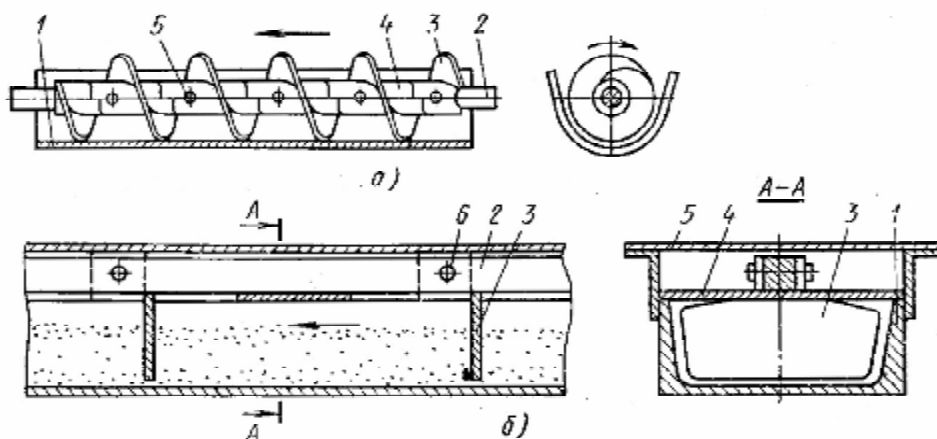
Шнековый (а) и скребковый (б) конвейеры для удаления стружки
